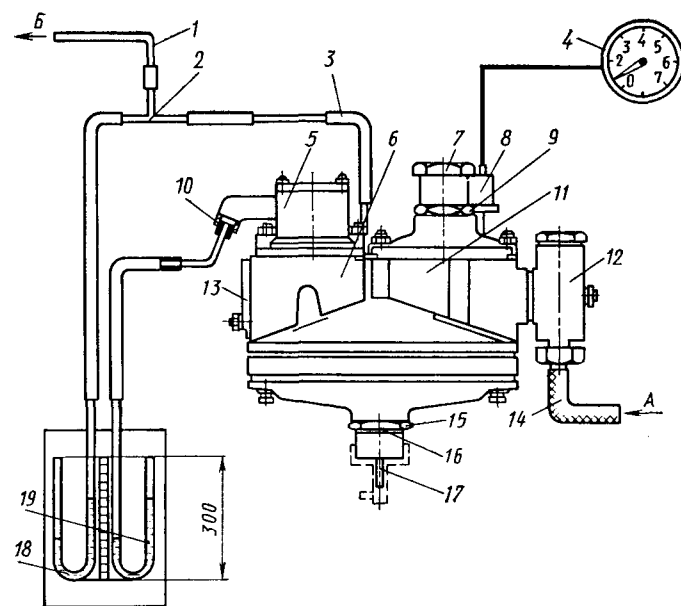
Схема соединения приборов для регулирования газового редуктора:
